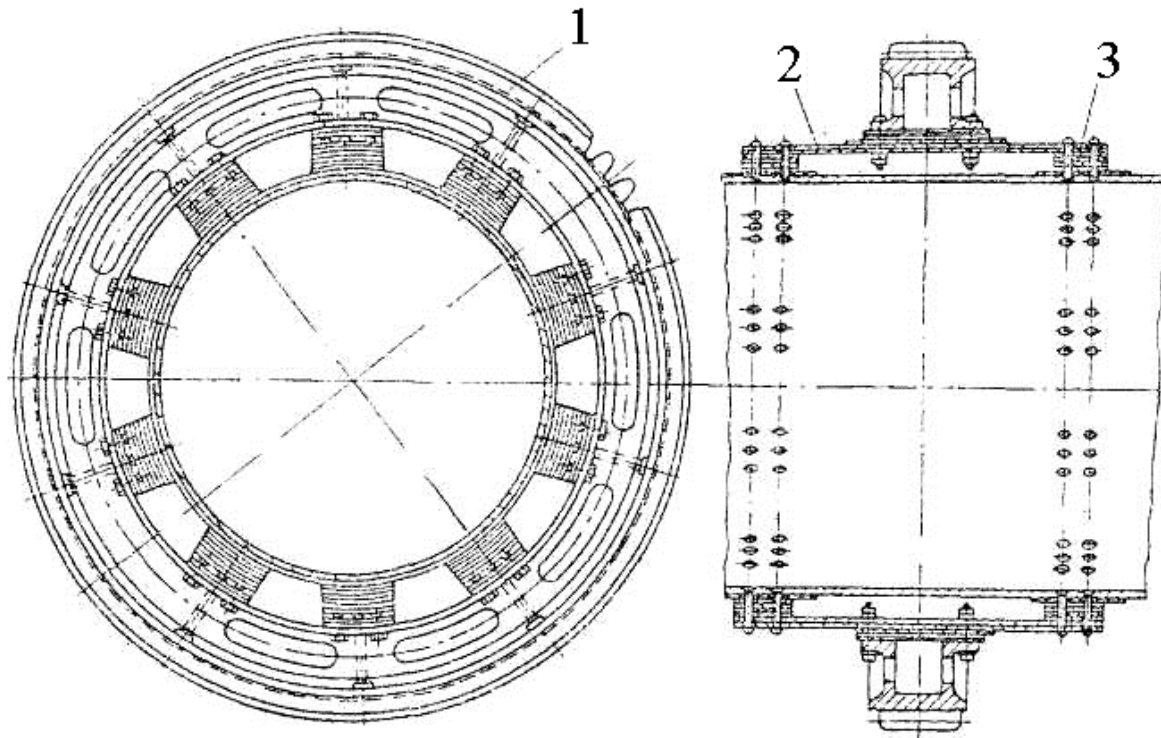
Крепление венцовой шестерни на пластинчатых пружинах:
